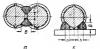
Схема измеряемых размеров сварных фланговых швов:
